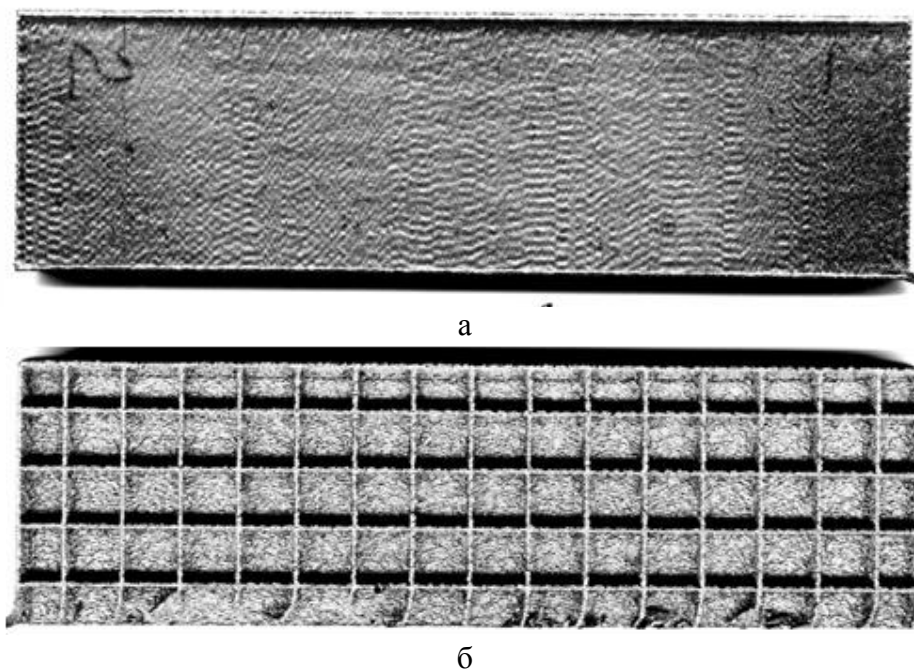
Опытный образец сплава ВТ6, изготовленный по технологии СИЭЛ:
